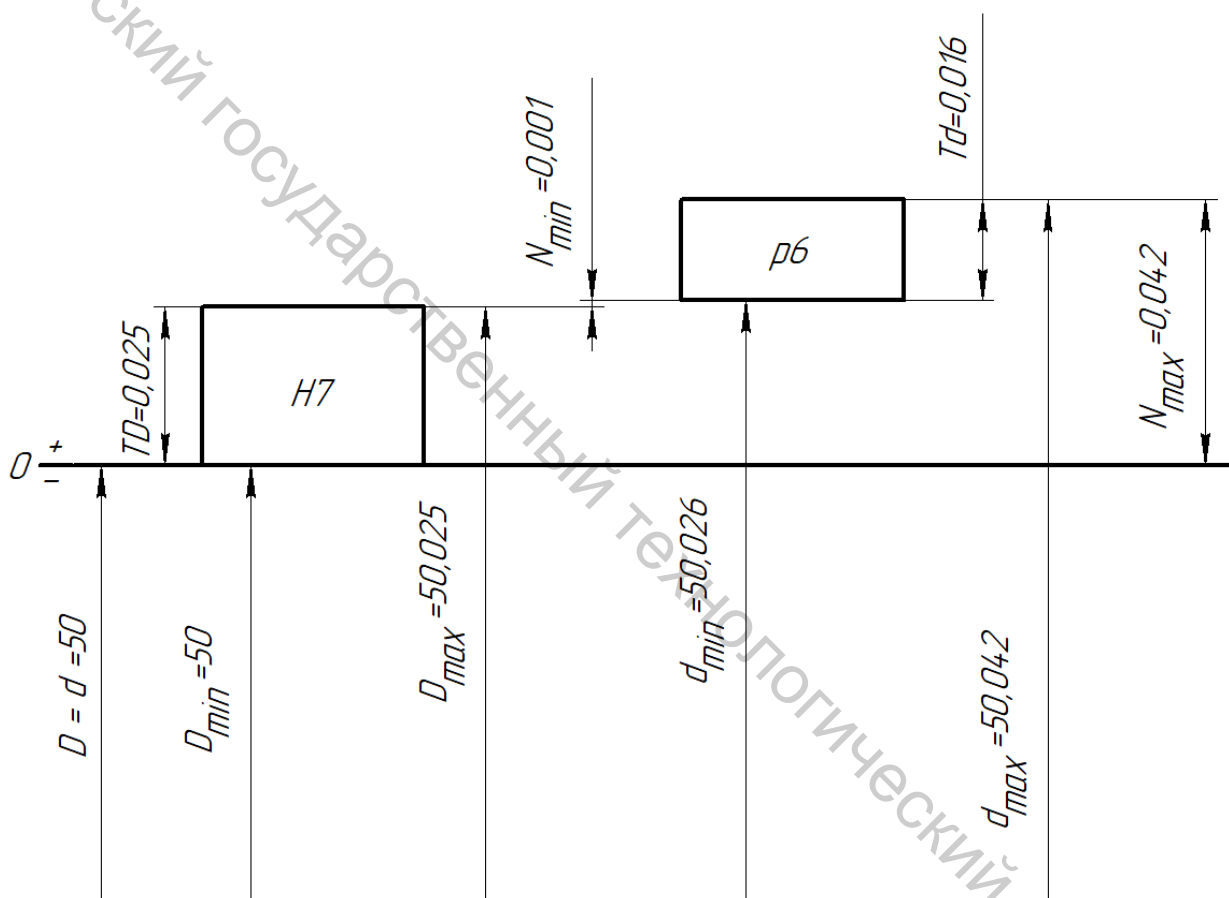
Схема расположения интервалов допусков в посадке
